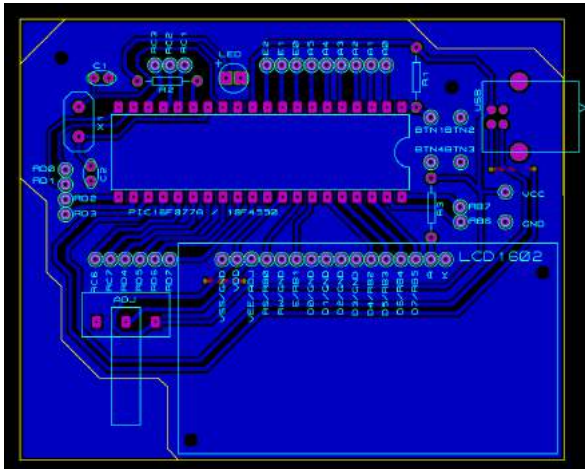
Diseño PCB de la tarjeta para el PIC16F877A.
